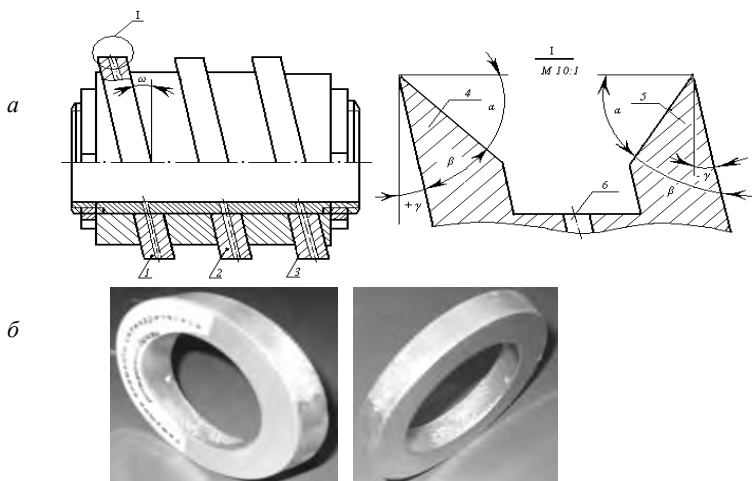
Цилиндрическая ротационная фреза (а), фото (б) опытных образцов режущего элемента из Р6М5: ω - угол наклона зуба фрезы; α - статический задний угол режущего клина; γ - передний угол режущего клина; β - угол клина
